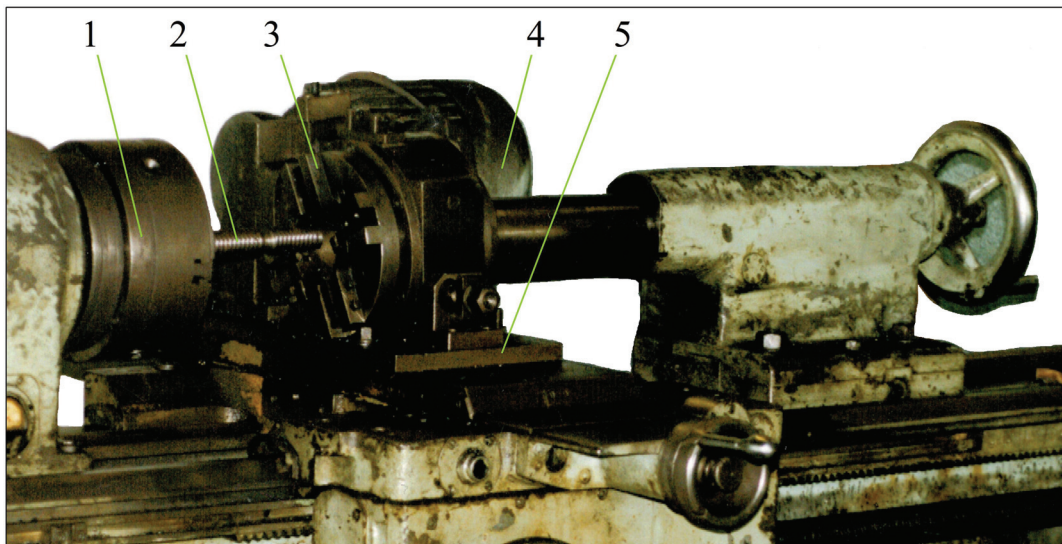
Приспособление для нарезания резьбы охватывающей фрезой:
